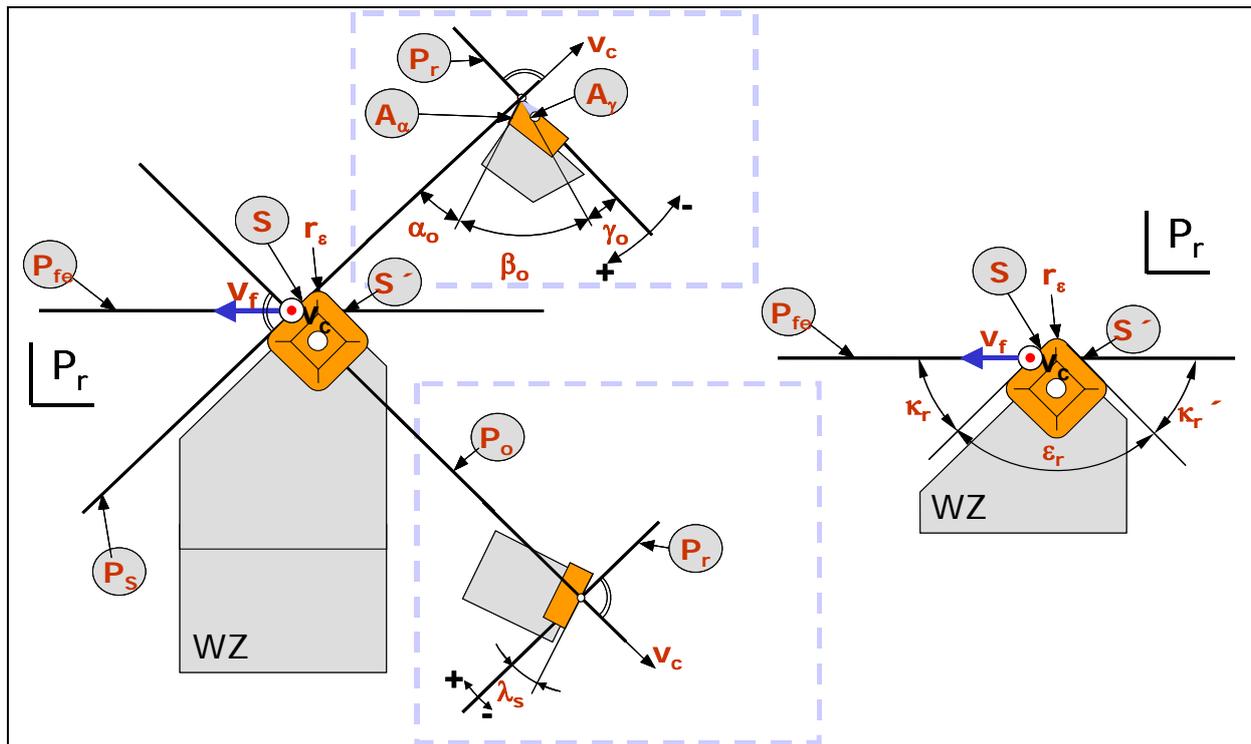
Bisher genutzte zweidimensionale Ansichten der Elemente am Drehwerkzeug
